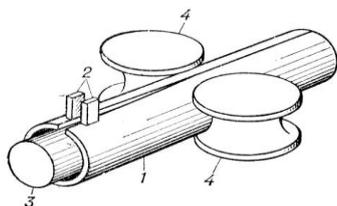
Схема сварки труб контактным способом: 1 — труба; 2 — скользящие контакты; 3 — сердечник; 4 — обжимные ролики.
